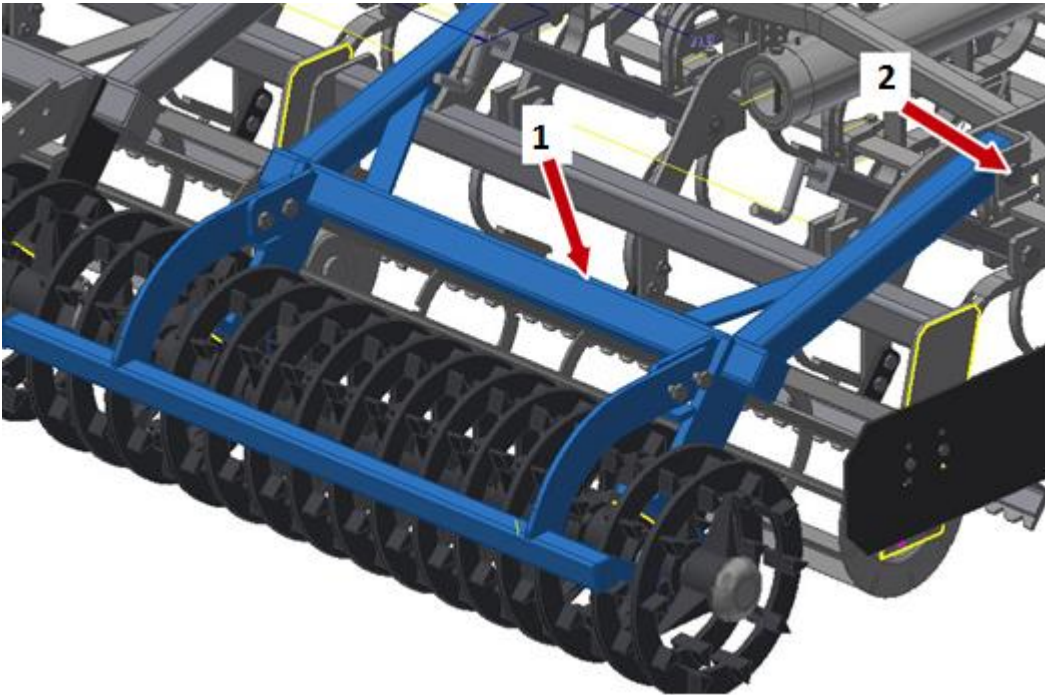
Montageansicht einer Stiftwelle für SHARP: 1 - Stiftwellenhalterung mit Armen, 2 - Schraube M20x135-8,8 + Mutter M20-8
